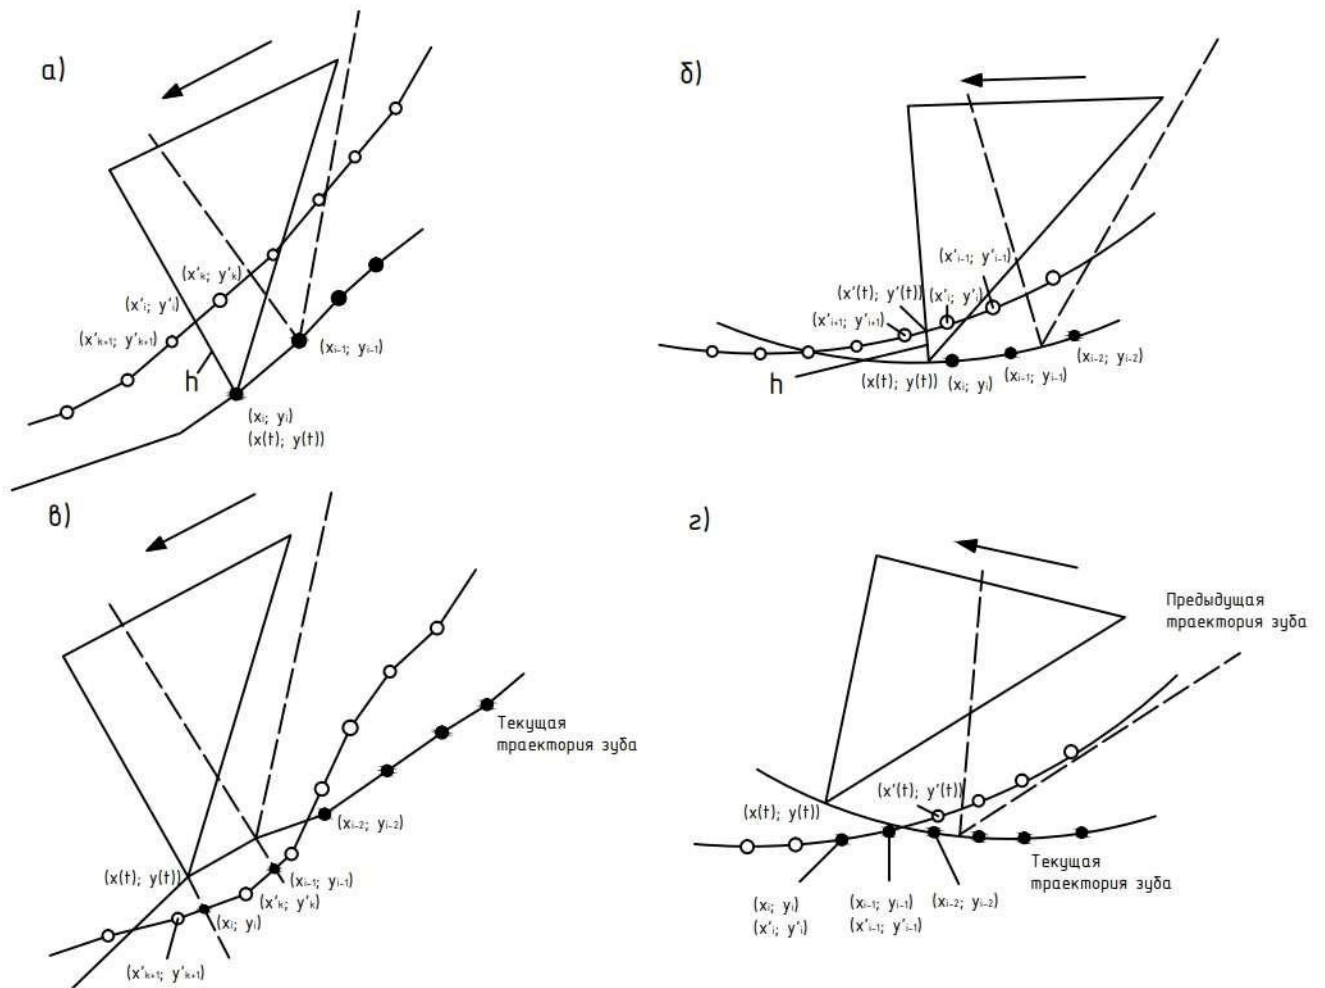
Алгоритм формирования поверхности: а – зуб фрезы находится в металле, б – зуб фрезы находится между выходом и врезанием, в – зуб фрезы находится за пределами обрабатываемого материала, г – зуб фрезы вышел из металла [36]
